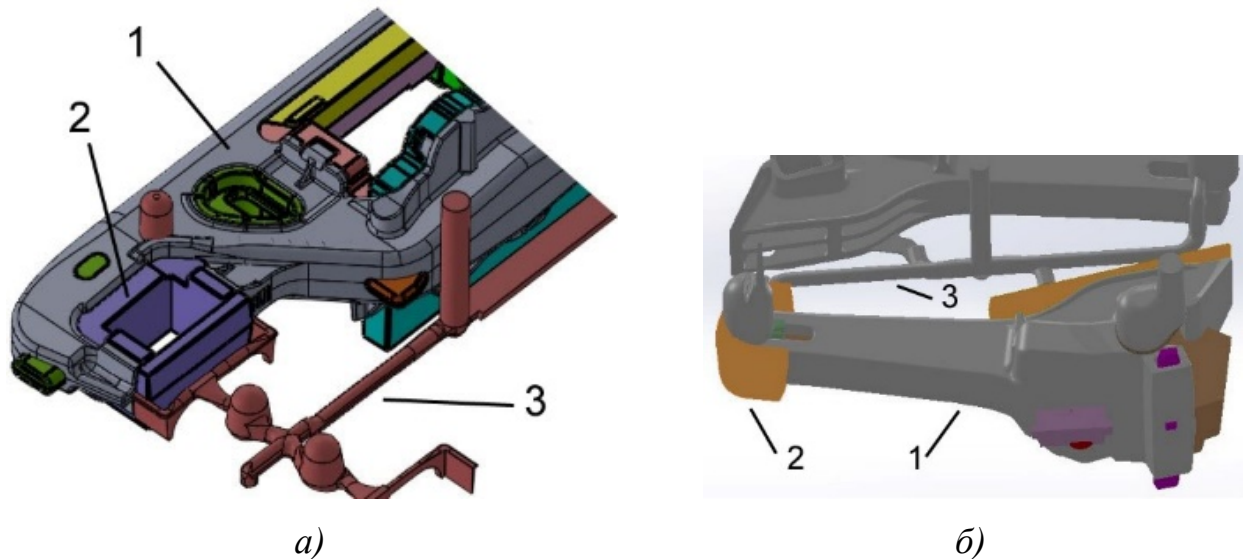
Эскиз отливки и элементов литейной формы (1 – отливка; 2 – стержень; 3 - ЛПС): а – «Рама боковая» (отливка симметрична); б – «Корпус автосцепки»
